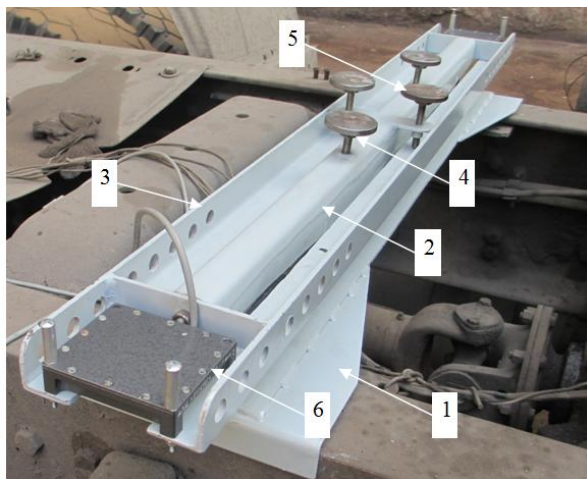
Приспособление для установки датчиков в нулевую отметку
